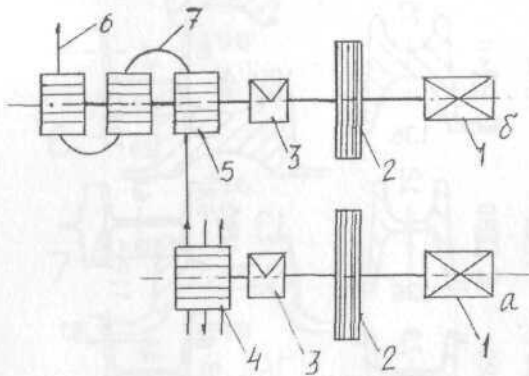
Двоступенчатий стан лінійного типу: 1-головний привід; 2- маховик; 3- шестерінчаста клітка; 4- заготовочна чорнова клітка; 5 - клітка чистової лінії; 6 - готовий профіль; 7 - обвідний апарат
